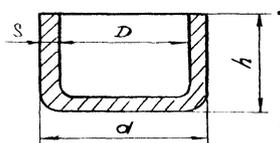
Эскиз штампуемой детали: *S* – толщина стенки детали;  $d$ ,  $D$  – диаметры наружной и внутренней поверхностей детали; *h* – высота колпачка
